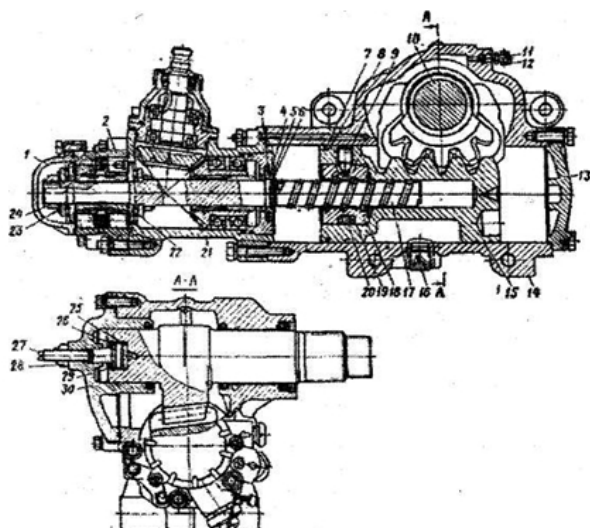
Рулевой механизм автомобиля КамАЗ-4310: 1,6,17 - крышки: 2-распределитель; 3 -уплотнения; 4 - вал сошки; 5 - перепускной клапан: 7-картер: 8 - поршень-рейка; 9 - сливная пробка; 10 - винт; 11-шариковая гайка; 12-желоб: 13-шарик; 14-угловой редуктор; 15 - упорный шарикоподшипник; 16, 18 - гайки; 19 - винт; 20 - регулировочное кольцо; 21 -упорное кольцо; 22-предохранительный клапан.
